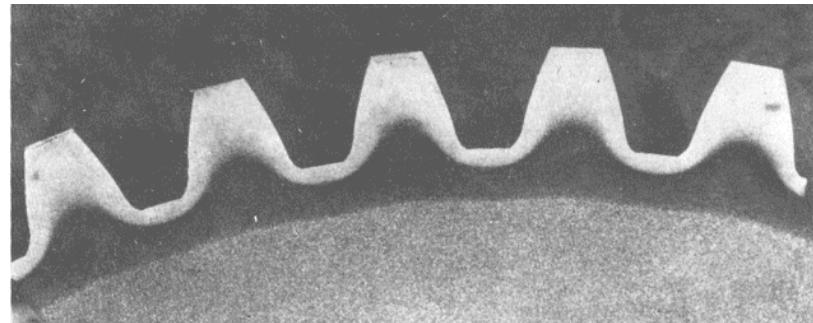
Макроструктура шестерни с неравномерным слоем и напряжениями, могущими вызвать поломку зубьев.
